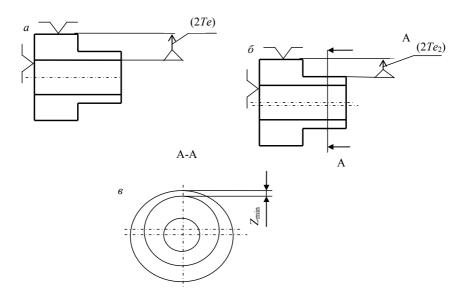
Схема образования неравномерного припуска: a — первая операция; δ — вторая операция; ϵ — схема неравномерного припуска
